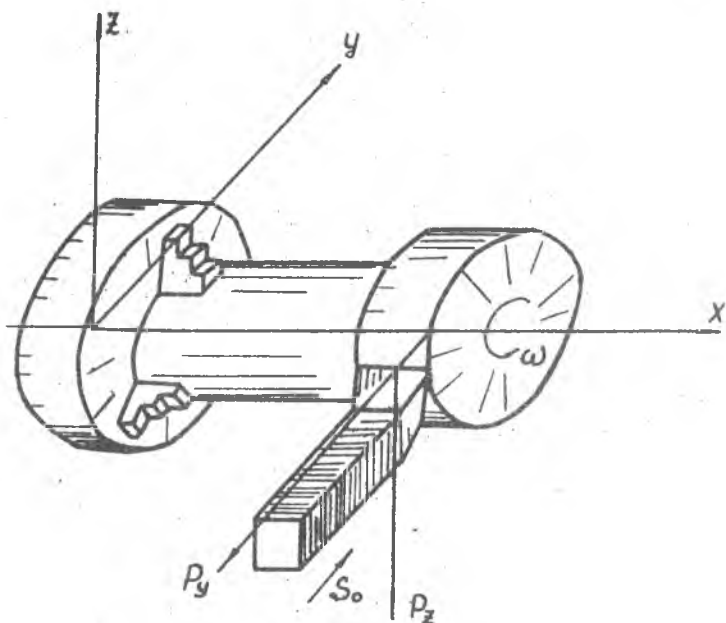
Рис. I Схема свободного течения кольцевого буртика лопаточным резцом
